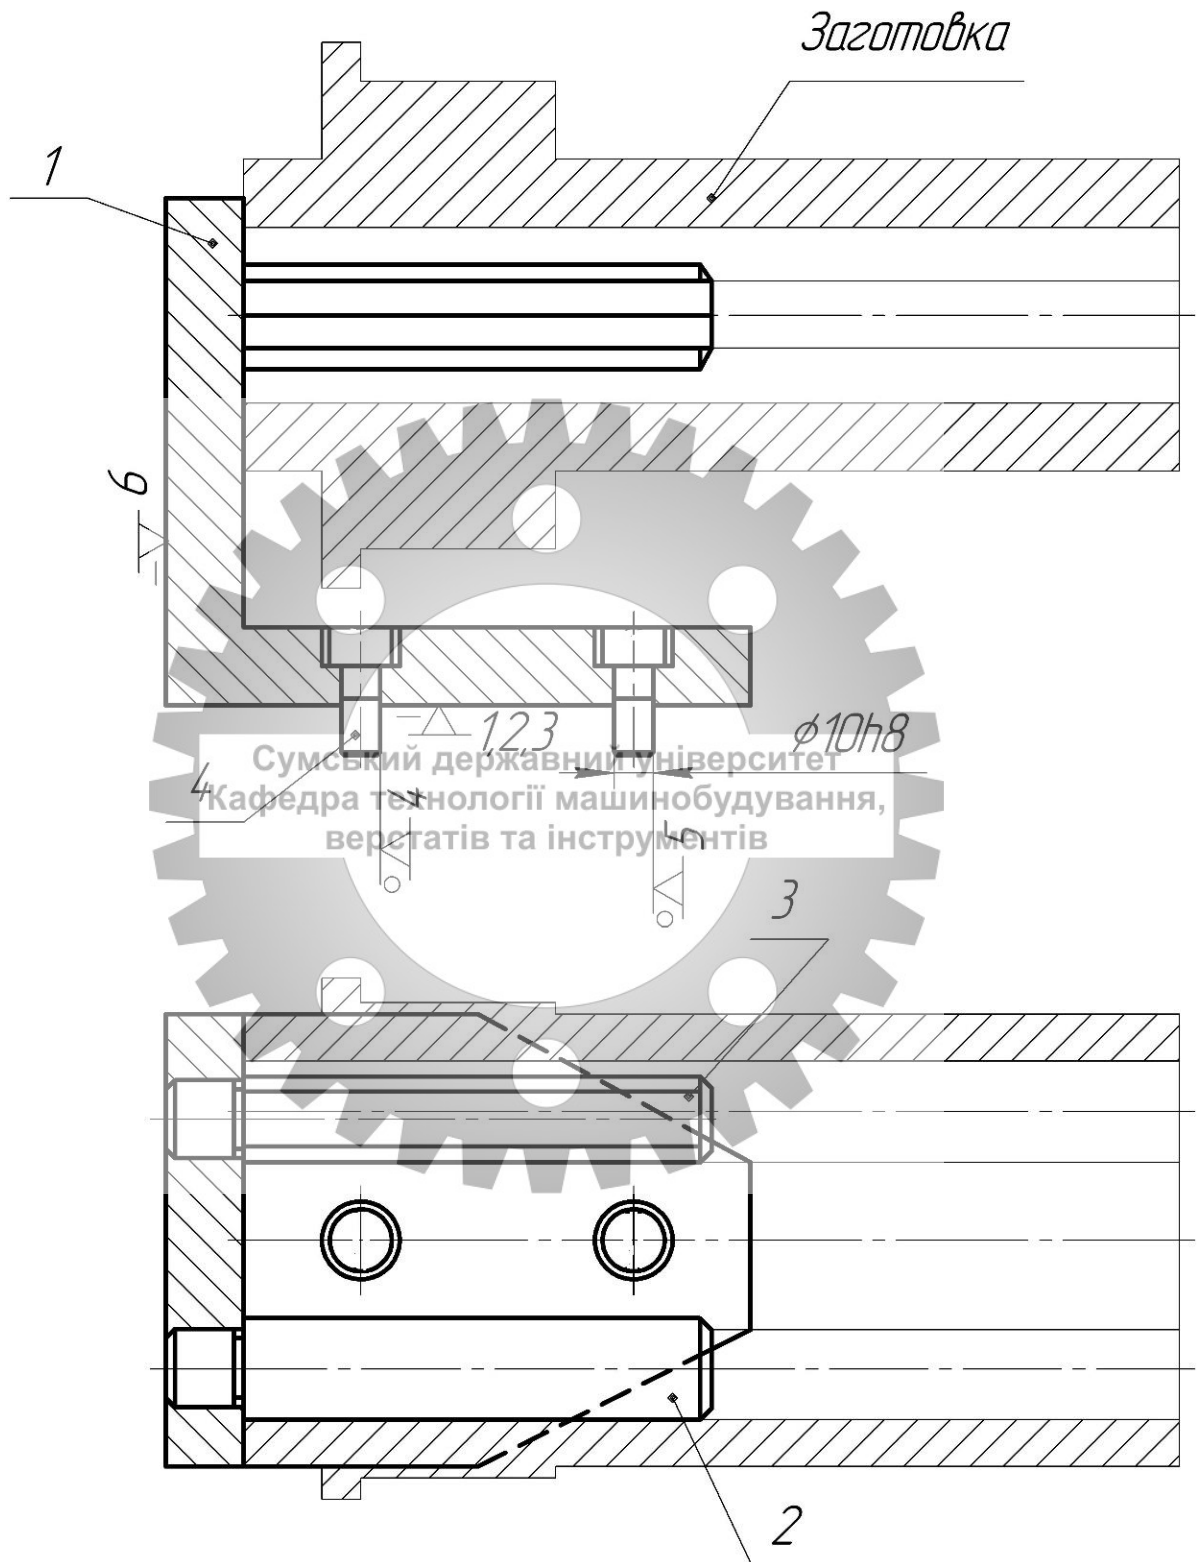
Ескіз складальної одиниці для установки заготовки на пальці:
